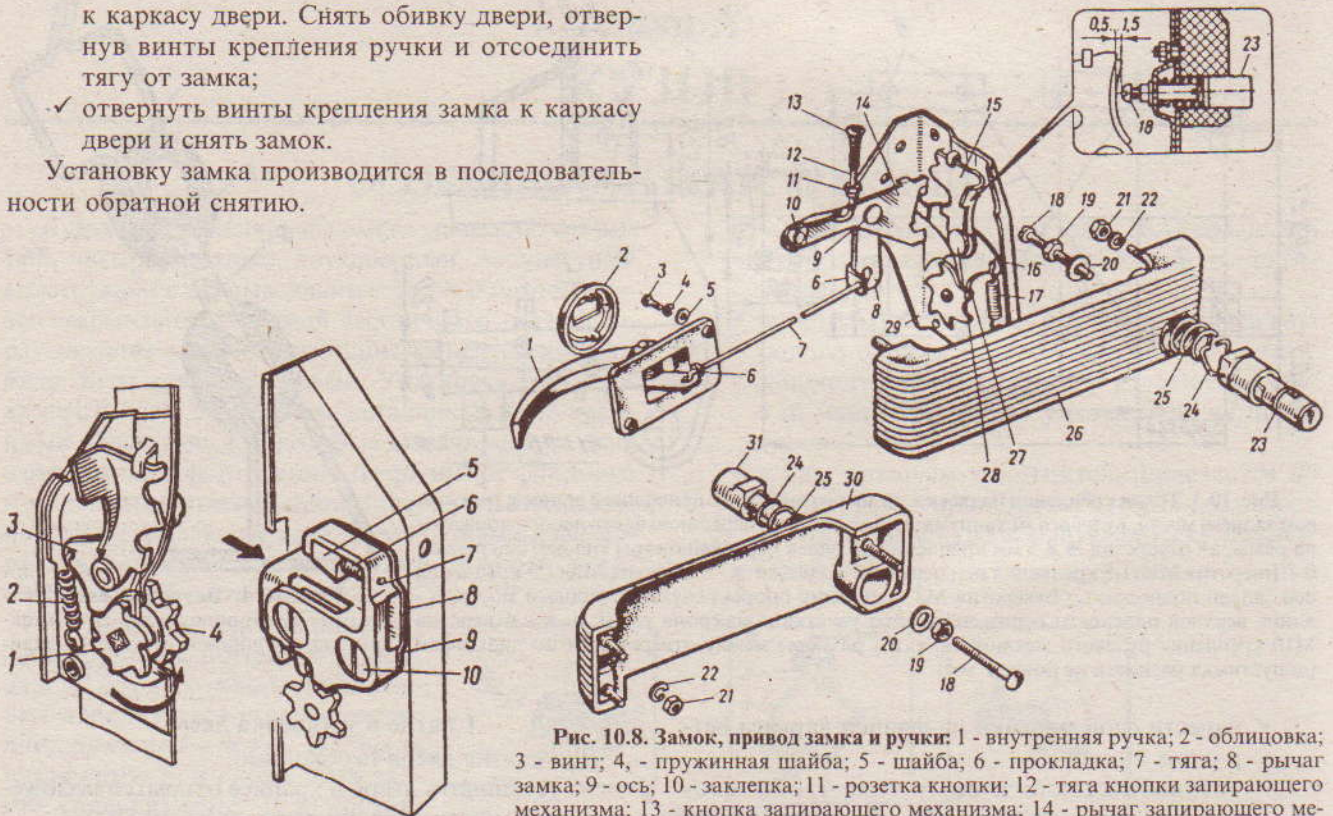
Положение замка и заселки при накрывании двери: 1 - храповик; 2 - пружина; 3 - собачки храповика; 4 - ротор замка; 5 - сухарь; 6 - пружина сухаря; 7 - ось; 8 - прокладка заселки; 9 - заселка; 10 - винт
